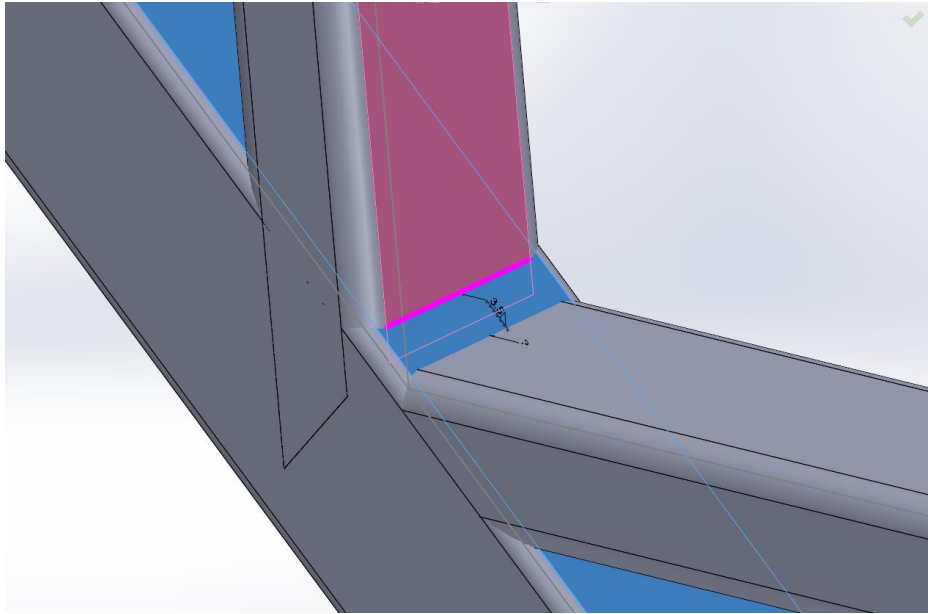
Paredes seleccionadas para ser soldadas
